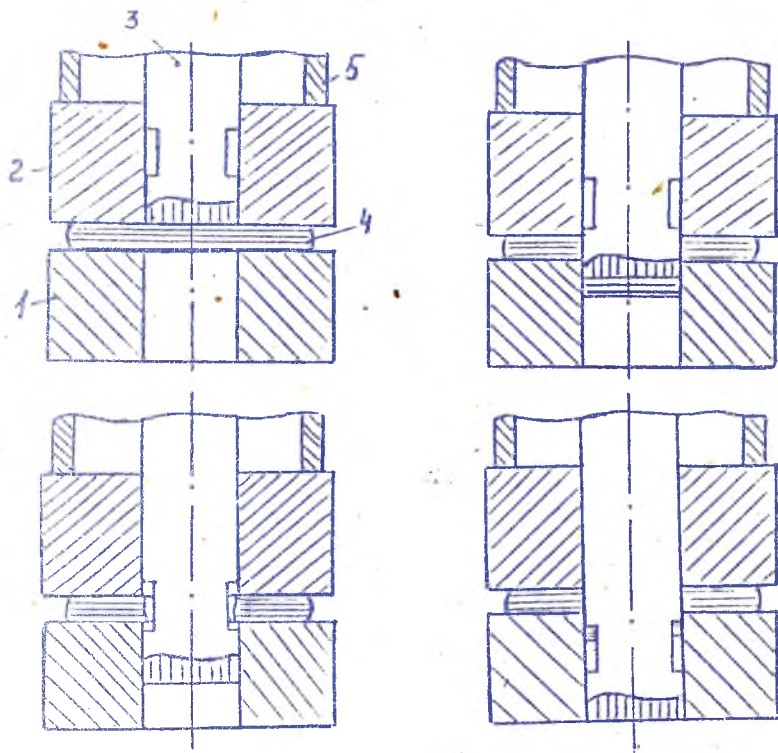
Устройство для пробивки отверстий в толстолистовых заготовках из ПКМ:
